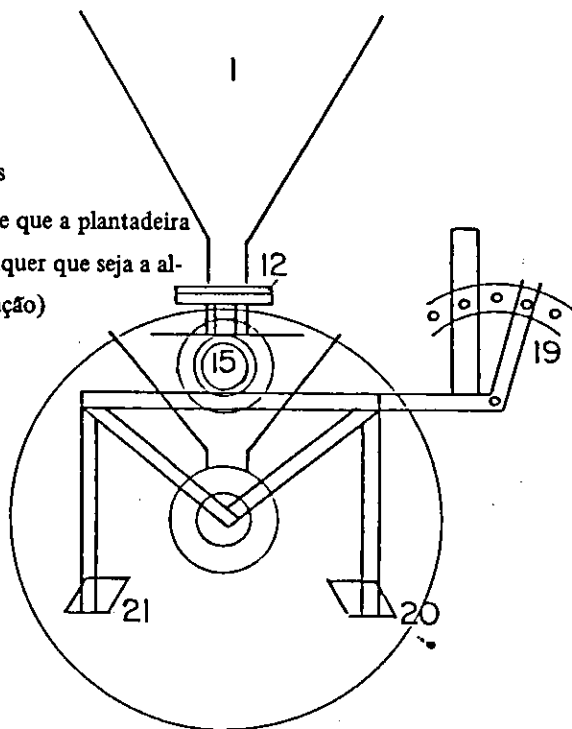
Esquema de montagem da plantadeira de alho para tração animal (vista lateral).
